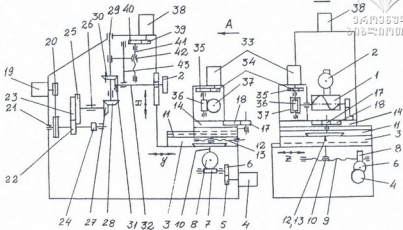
Кинематическая схема станка с ЧПУ для нарезания цилиндрических червяков
